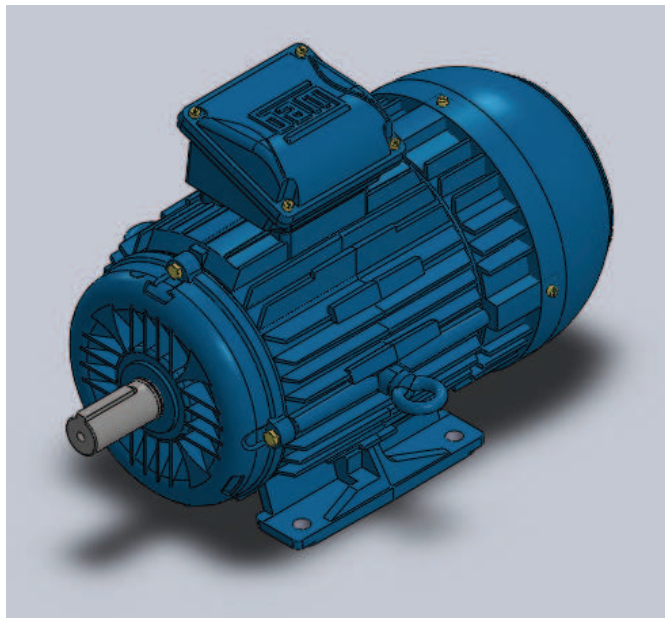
Gerador Elétrico WEG – W22 Premium
